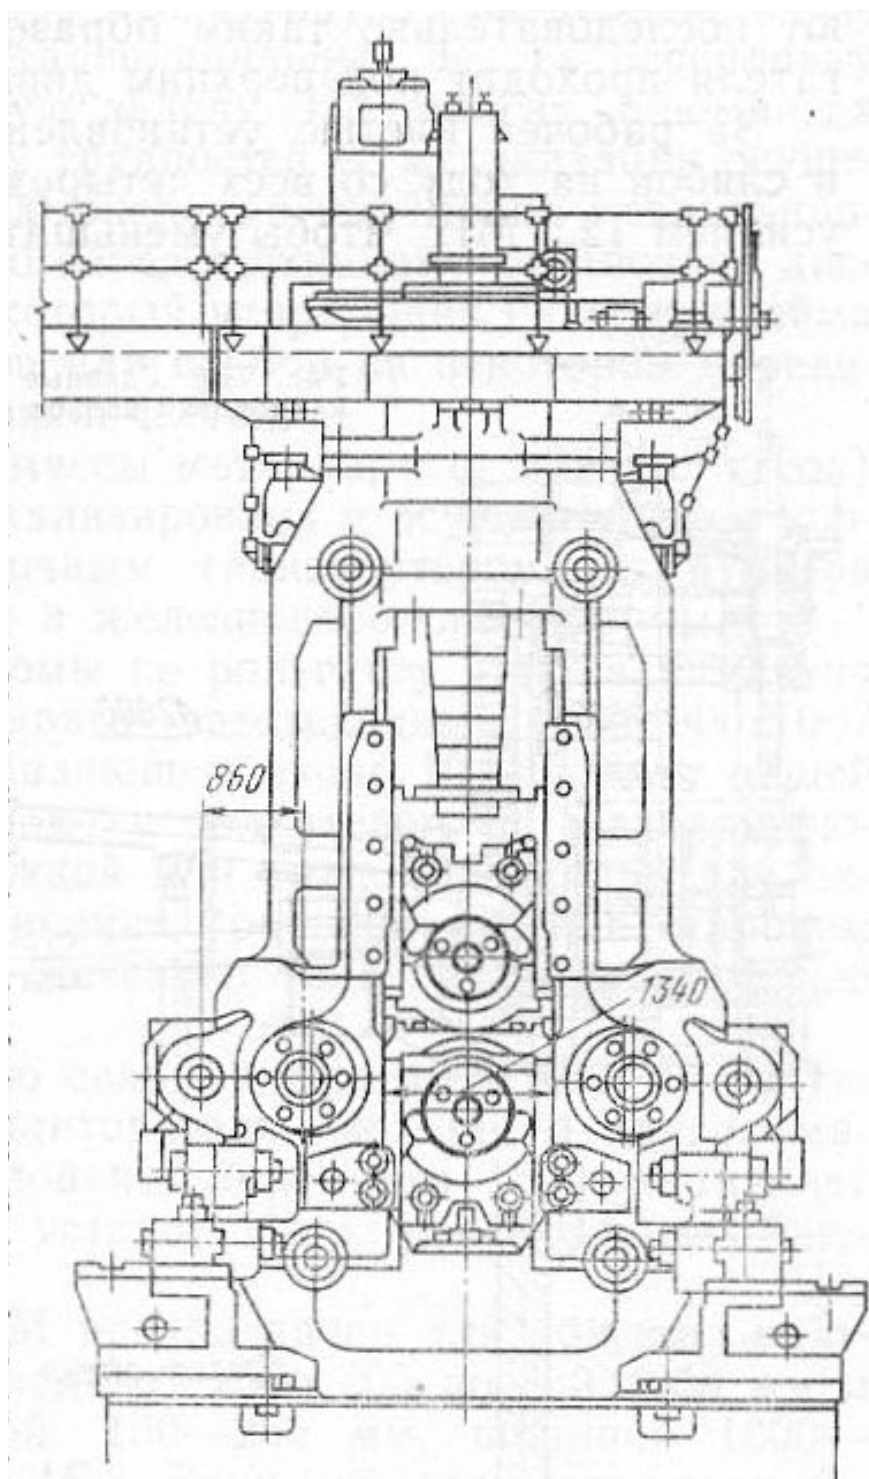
Робоча клітці слябінга 1150 (вид з боку)
